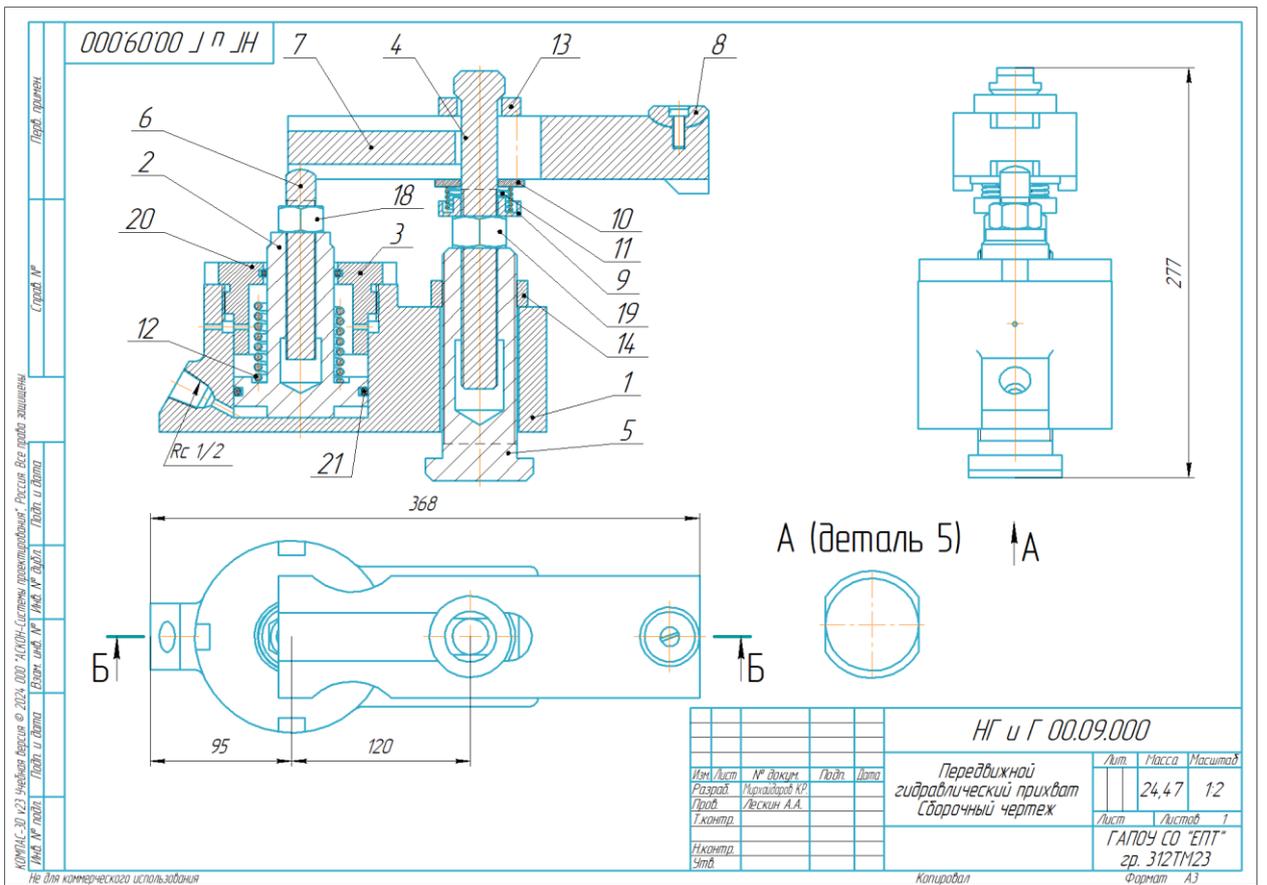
Схема сборки по сборочному чертежу " Передвижной гидравлический прихват"
